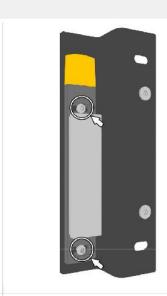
Ankerplatte an Montageplatte anbringen und Schrauben M6 x 8 mm Torx festziehen.
